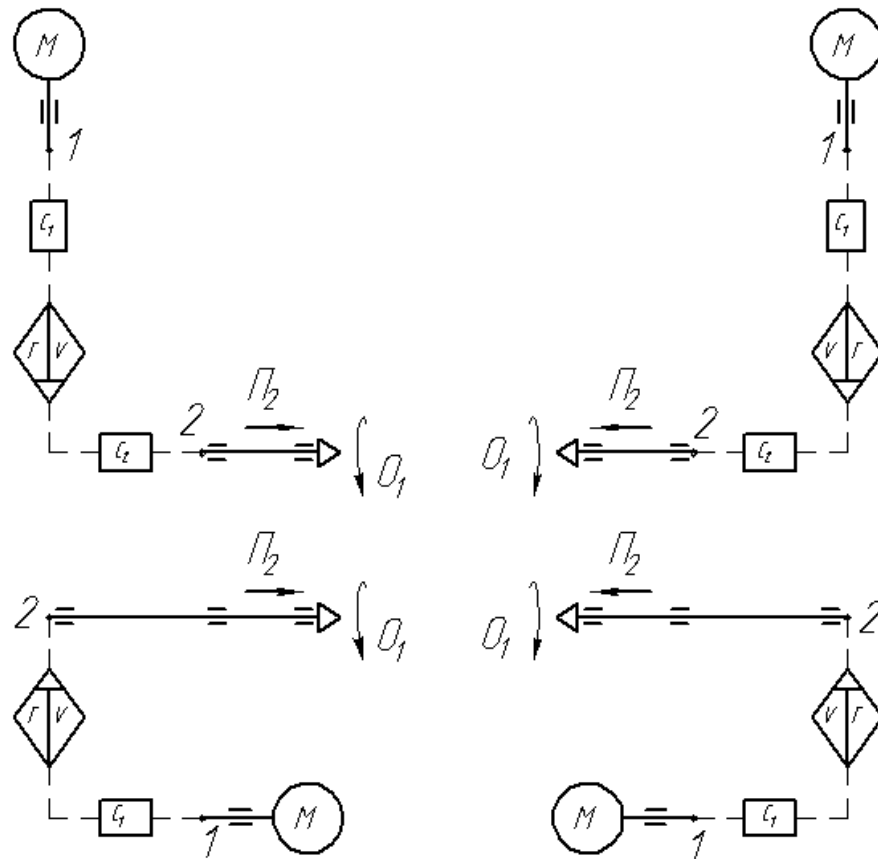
Структурно – кінематична схема фрезерно – центрувального напівавтомата
